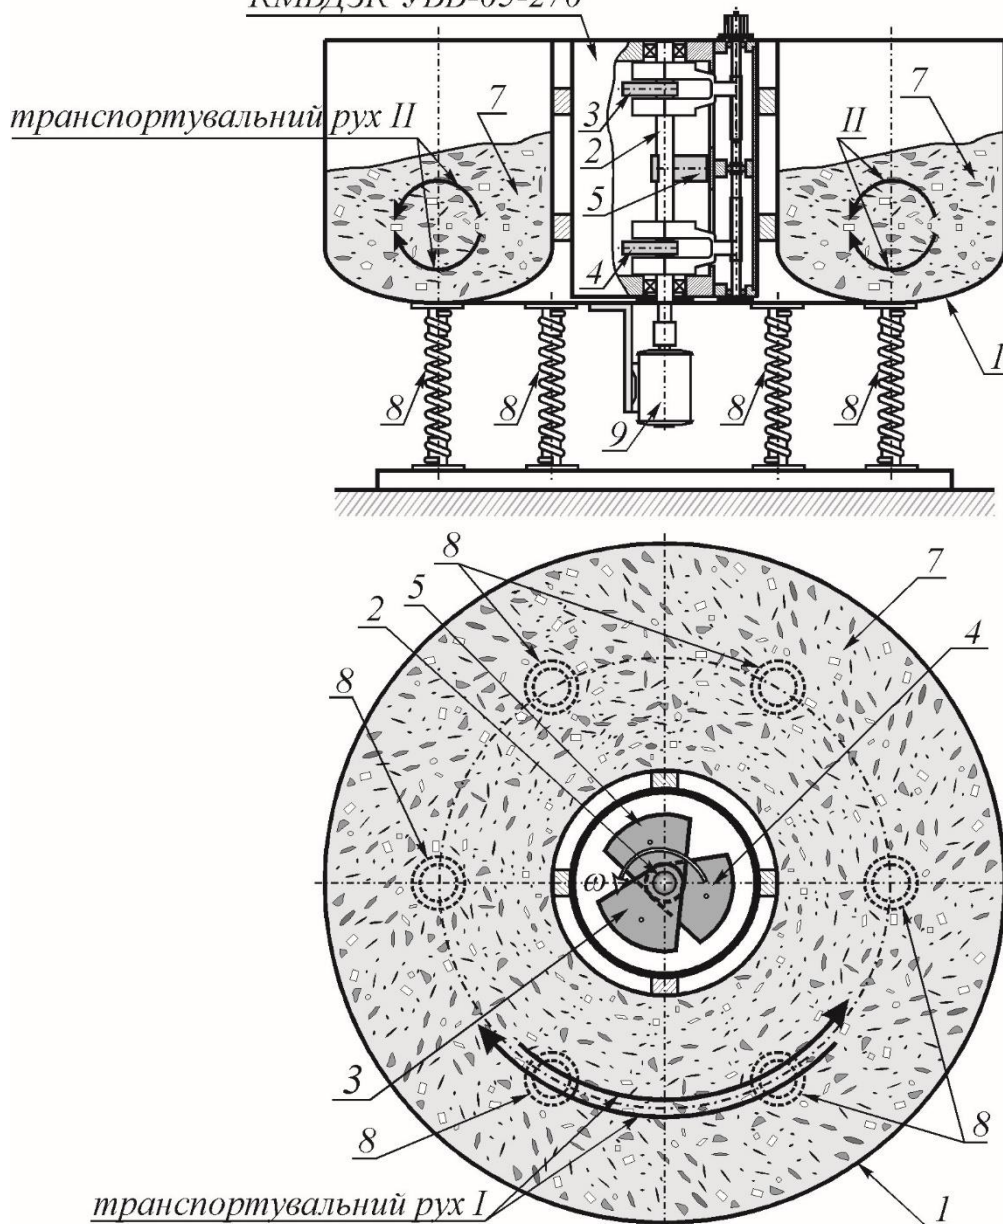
Вібраційний змішувач з торовою робочою камерою
